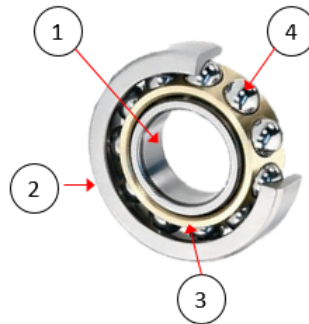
Componentes de un rodamiento: 1. Pista interna, 2. Pista externa, 3. Jaula, 4. Bola
